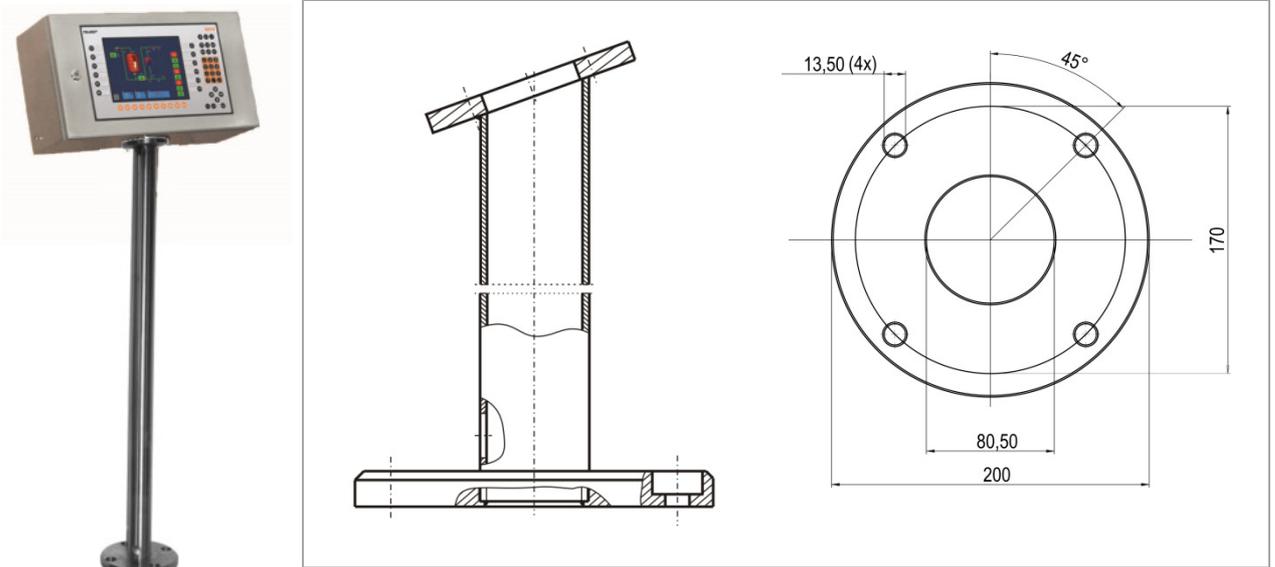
Standfuß - Bohrbild Bodenplatte
